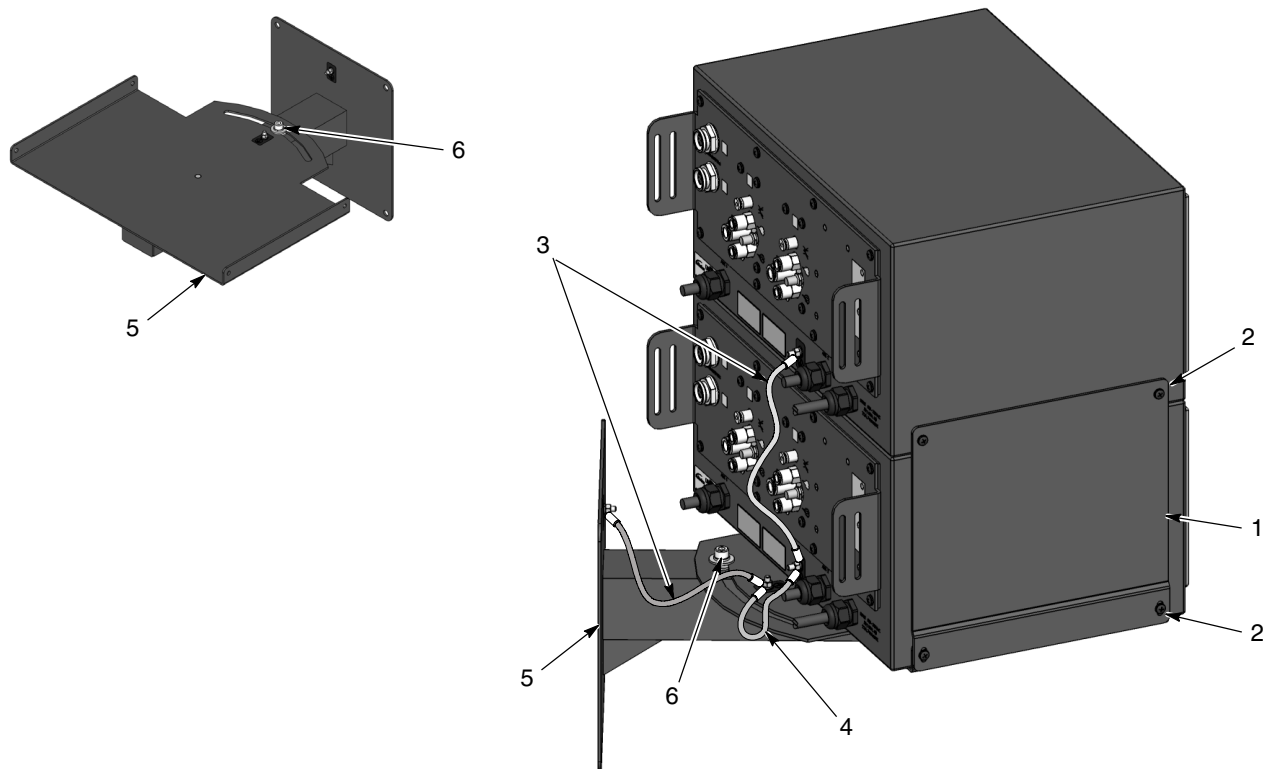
Montaje del controlador doble con soporte opcional de montaje en pared
